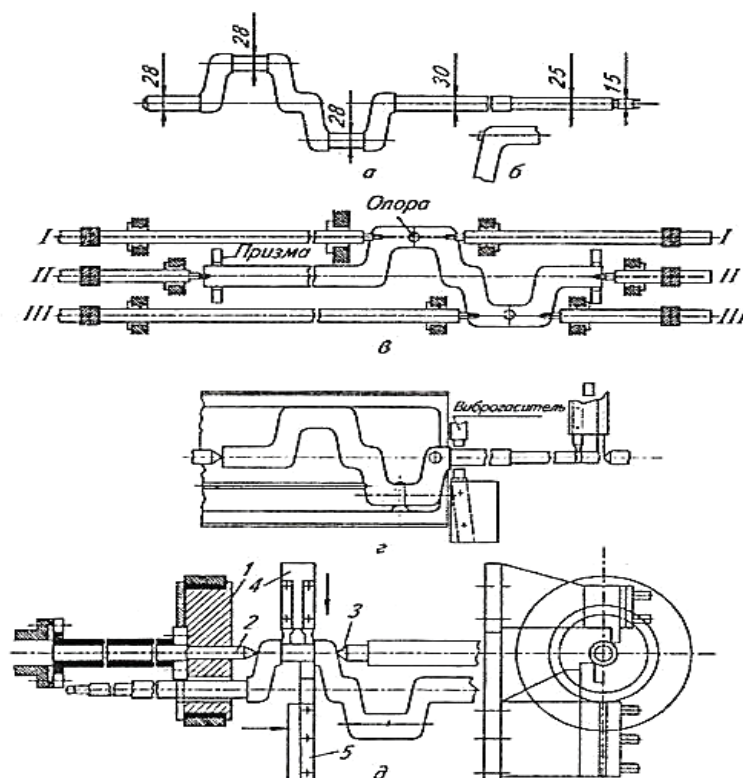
Схема обработки коленчатого вала: а – чертеж вала; б – бобышки для зацентровки; в – центровка вала; г – точение длинного конца вала; д – точение шеек; 1 – патрон; 2 – передний центр; 3 – заданный центр; 4 – резцедержатель продольного суппорта; 5 – резцедержатель поперечного суппорта
